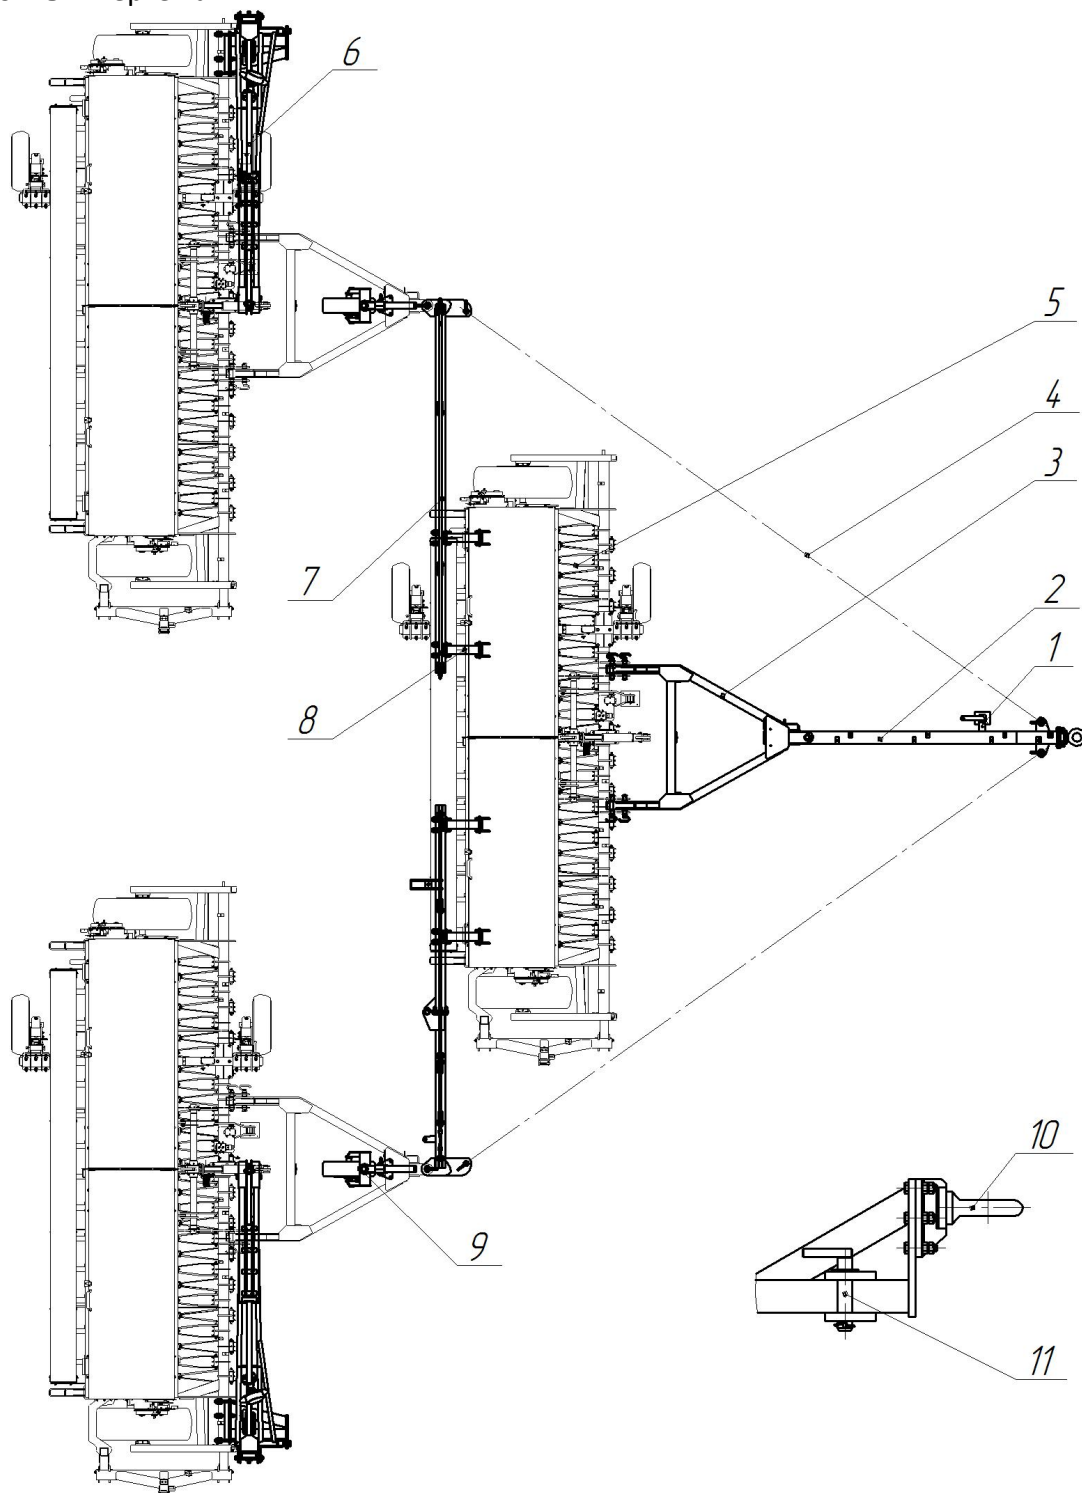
Широкозахватный посевной агрегат УС-3 + 3хЗС-42
